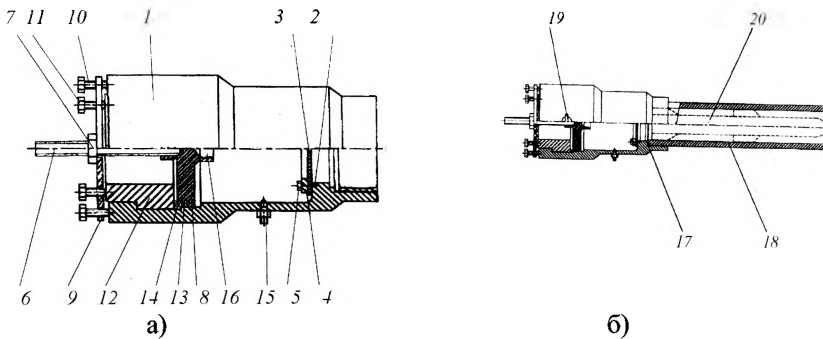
Устройство герметизации камеры высокого давления баллистической установки:
